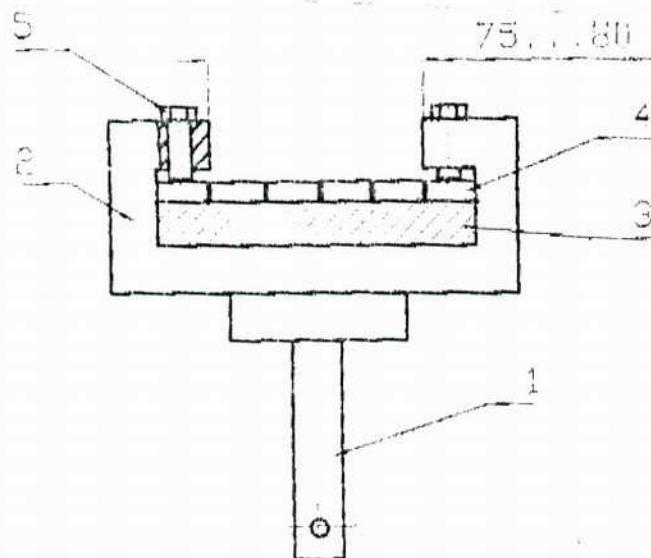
Рис. I Образец трубы с покрытием для испытаний на отслаивание покрытия
